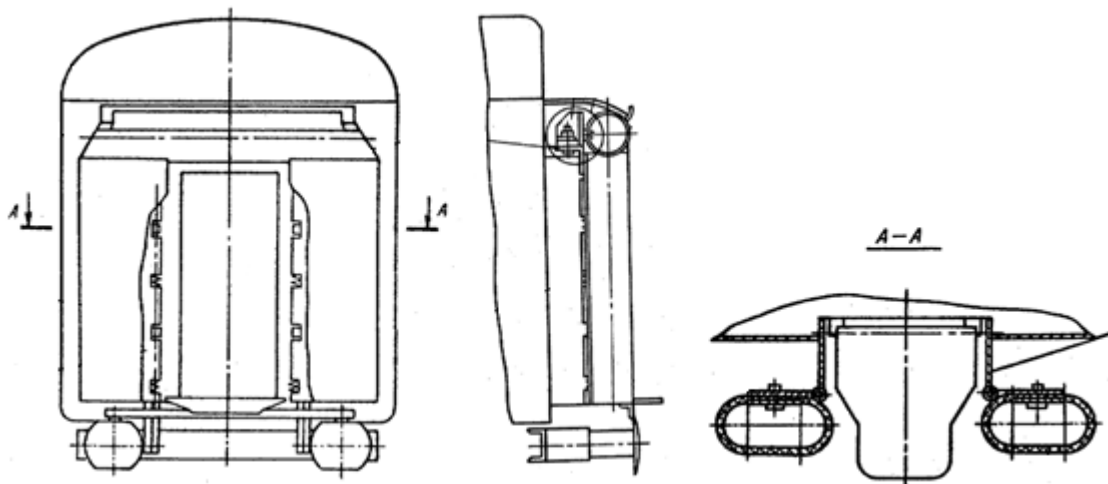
Загальний вигляд пружного огороження з поворотними створками
